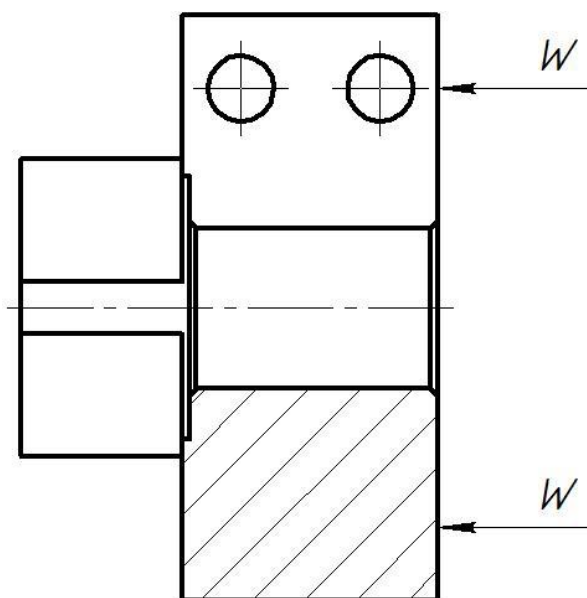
Принципиальная схема зажима заготовки в приспособлении с указанием мест приложения силы зажима.
